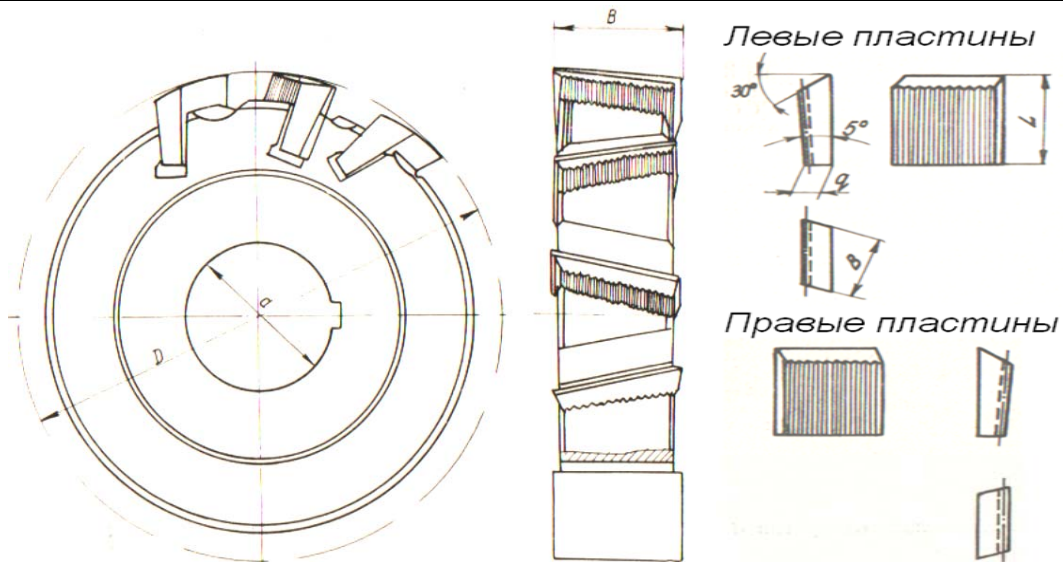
Сборная дисковая фреза с механическим креплением быстрорежущих пластин клиновидной формы с рифлениями, фиксирующими их положение в гнезде
